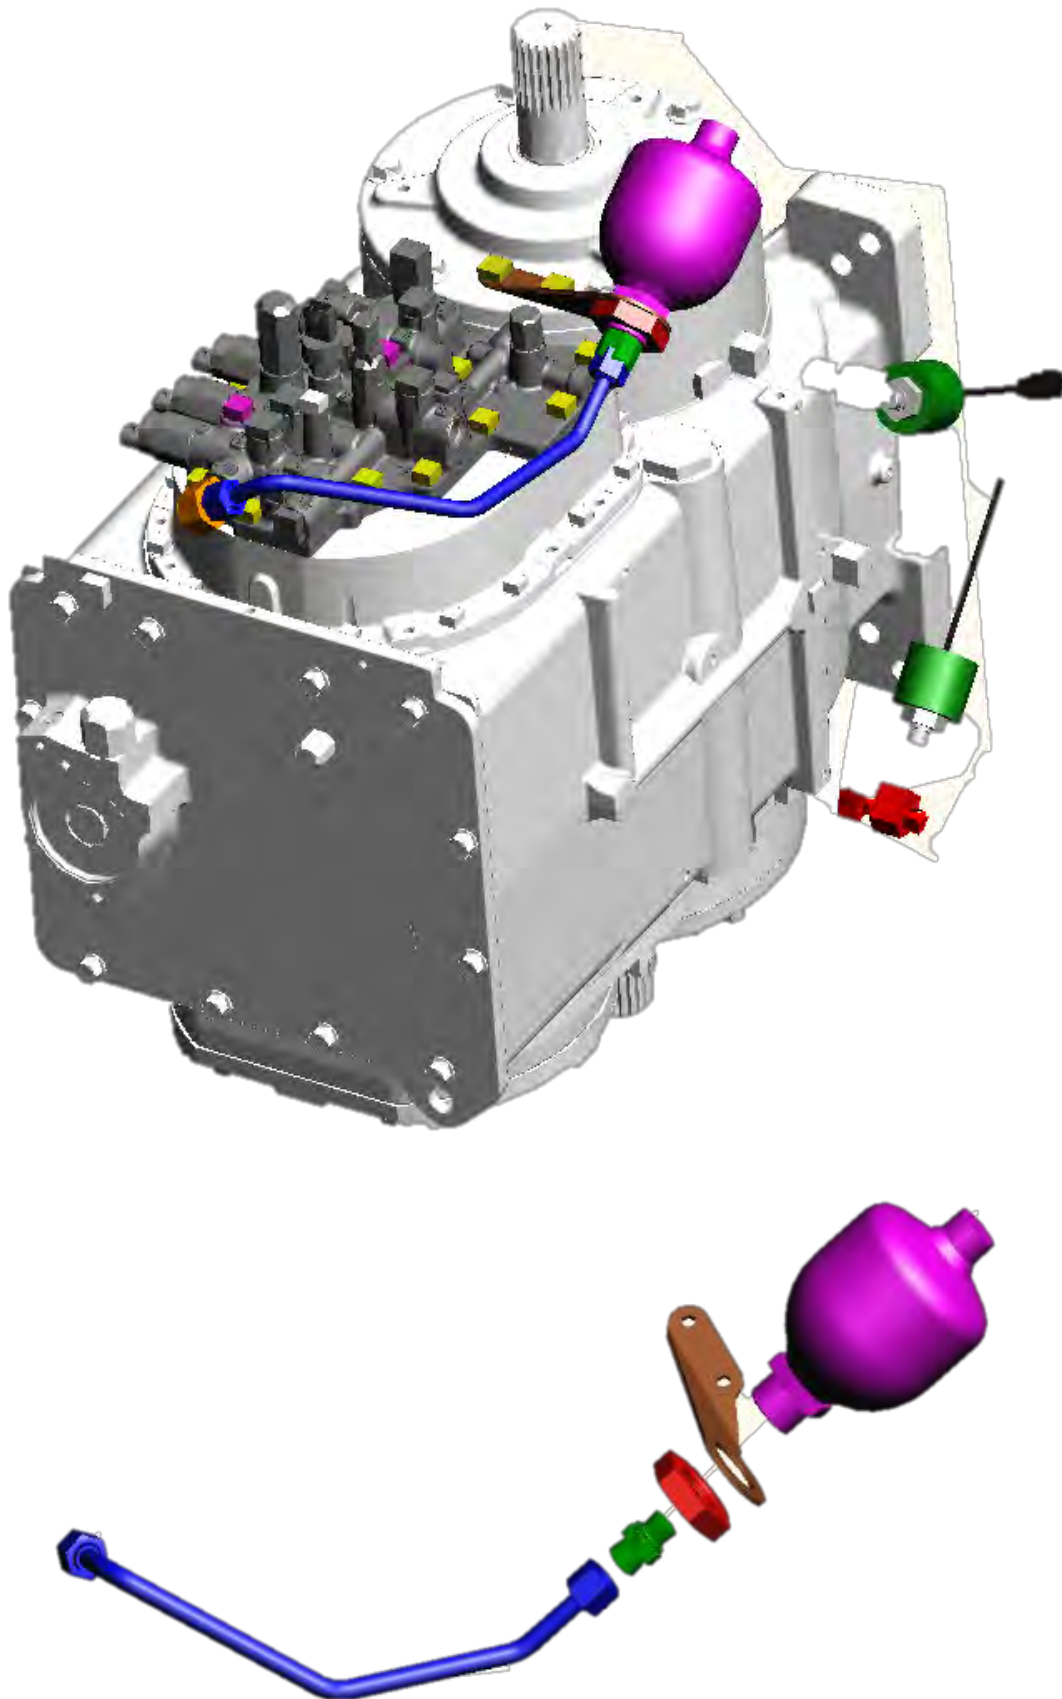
“Explosionado del proceso de montaje de la estación 6”
